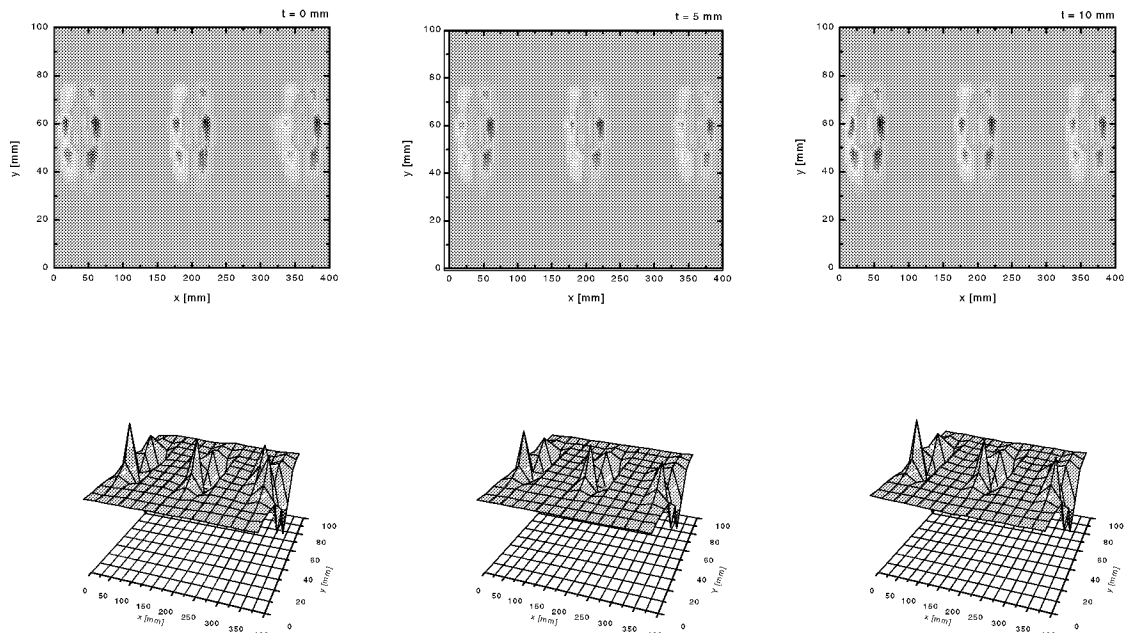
Messung dreier Nietbohrungen des Durchmessers 25 mm in einer Aluminiumplatte der Dicke 30 mm. Die mittlere Bohrung war fehlerfrei, die rechte mit einem Riß der Länge 10 mm, die linke mit einem Riß der Länge 20 mm behaftet. Die Platte mit dem Riß lag in zunehmender Tiefe ($t = 0, 5$ und 10 mm).
